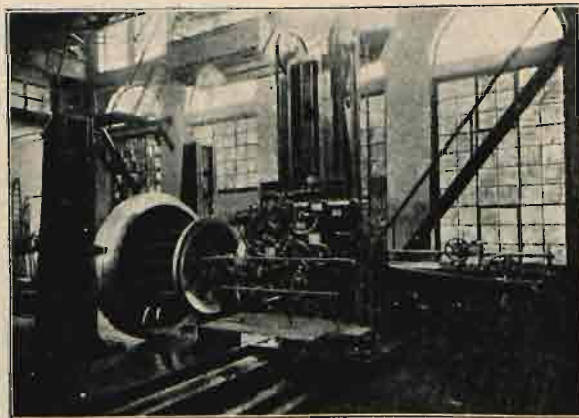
przedstawia turbiny dla zakładu w Finsing podczas ich montażu w warsztatach fabrycznych firmy F. Neumeyer, w Monachjum. W rysunku 18 podano zaś przekrój jednowirnikowych turbin spiralnych o wale pionowym, przeznaczonych dla zakładów o sile wodnej w Aufkirchen i w Eitting. Każda z tych turbin wytwarza pod spadkiem 25 m 13.000 koni mechanicznych. Pod względem przestrzennych wymiarów należą te turbiny do największych turbin spiralnych, jakie kiedykolwiek zbudowano.
